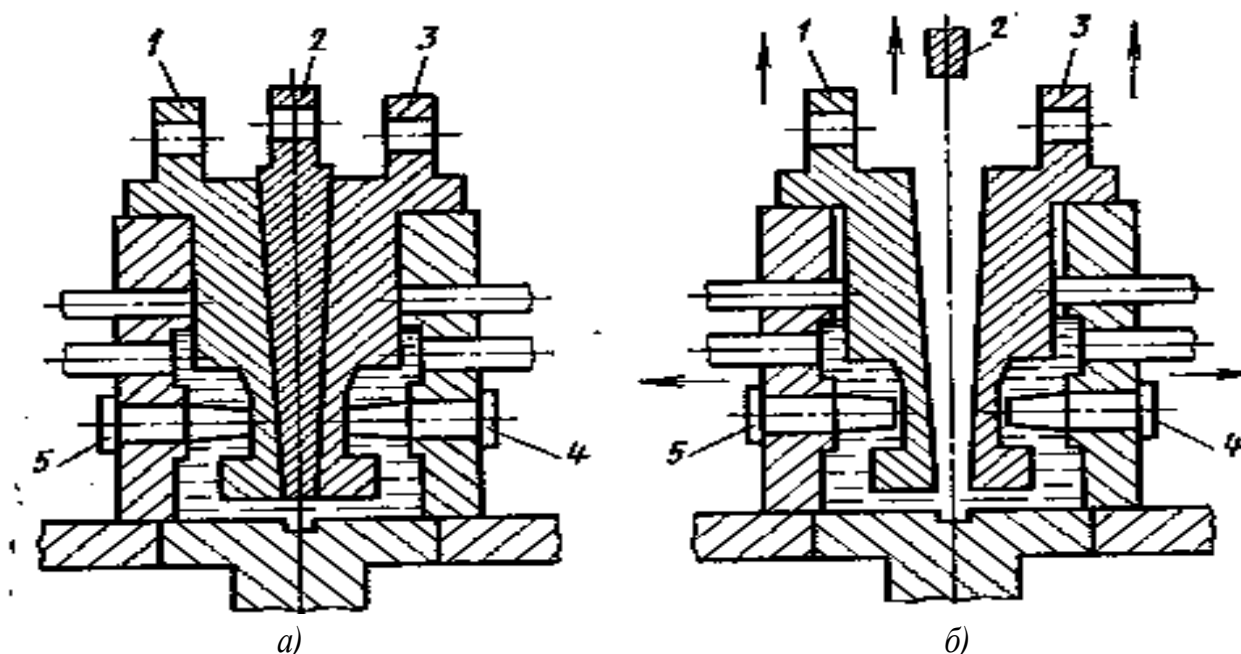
Кокиль для отливки поршня с разъемным металлическим стержнем.
